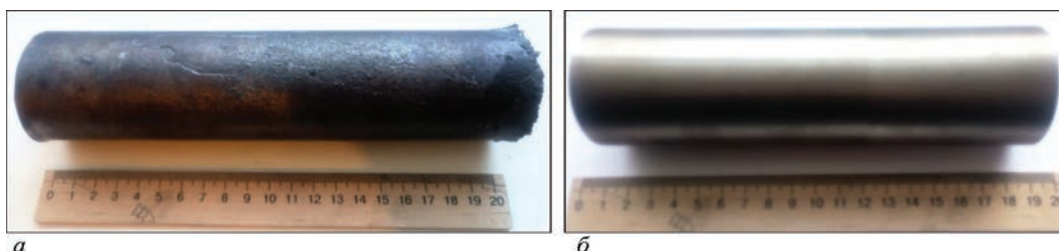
Вид зливка сплаву після виплавлення (а) і механічної обробки (б)
